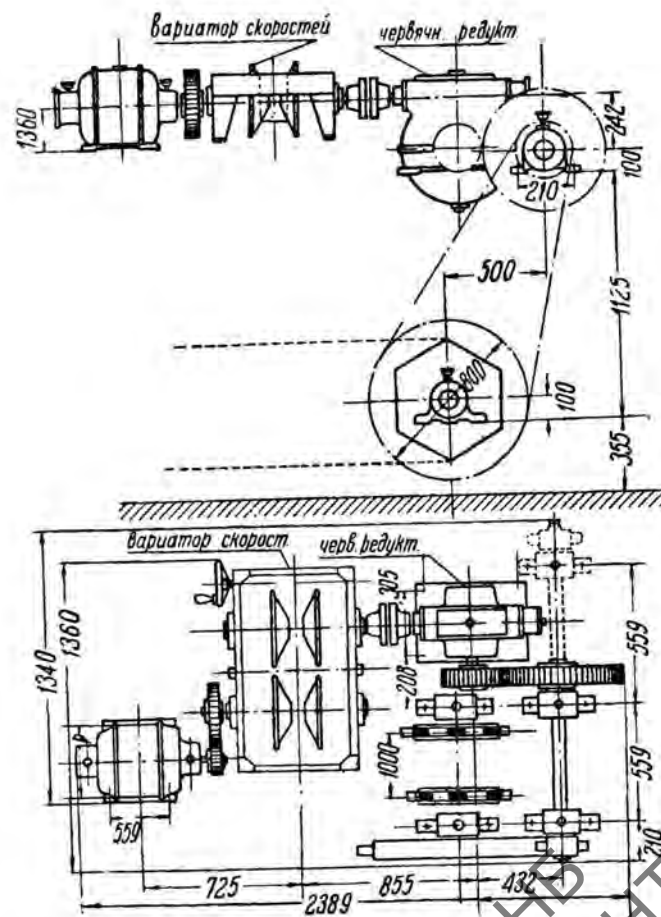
Схема привода для цепей с двойной зубчатой передачей Шахтогостроя.
